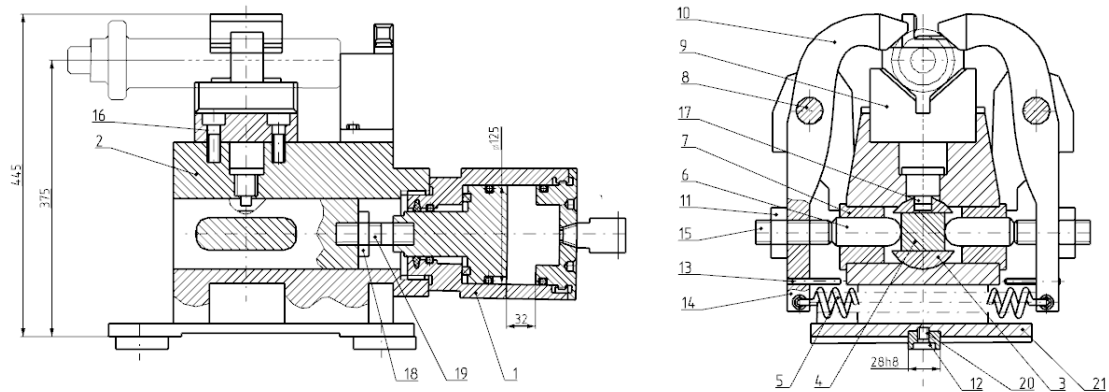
Пристосування для фрезерування шпоночного пазу
